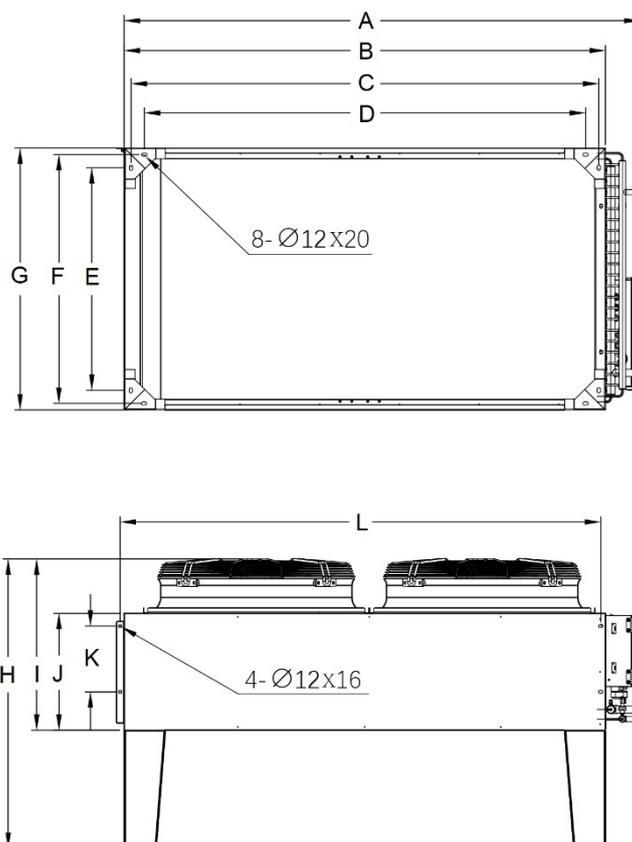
Габаритные размеры стандартного конденсатора серии CS с двумя вентиляторами
